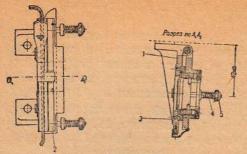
Фильмовый канал: 1—рамка; 2—дверца; 3—направляющие; 4—пружина; 5—гайка
